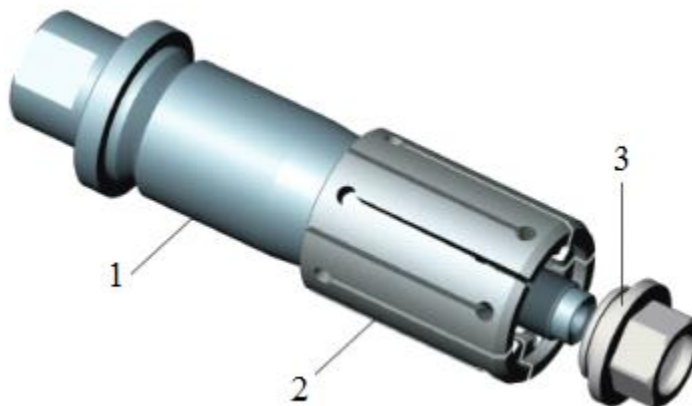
Оправка MZS фірми Roehm Spannzeuge з ручним затиском-розтиском
